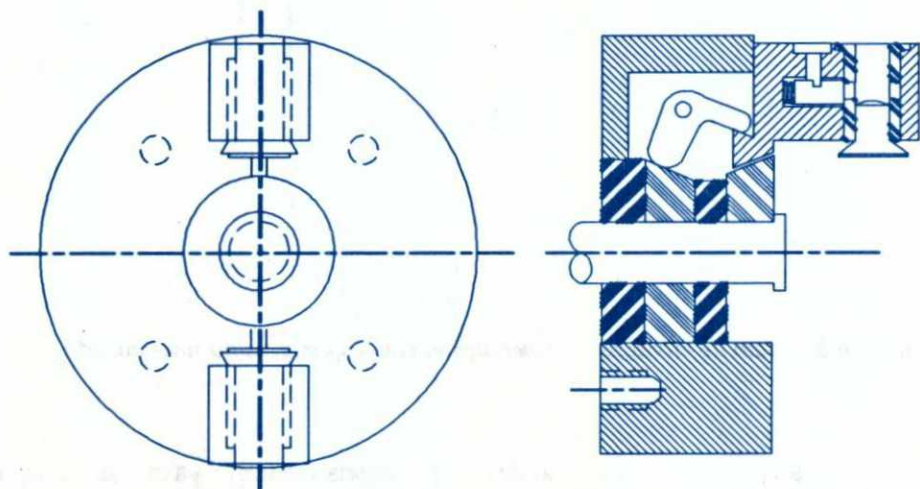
Plato autocentrante para maquinado de piezas tipo cruceta.
